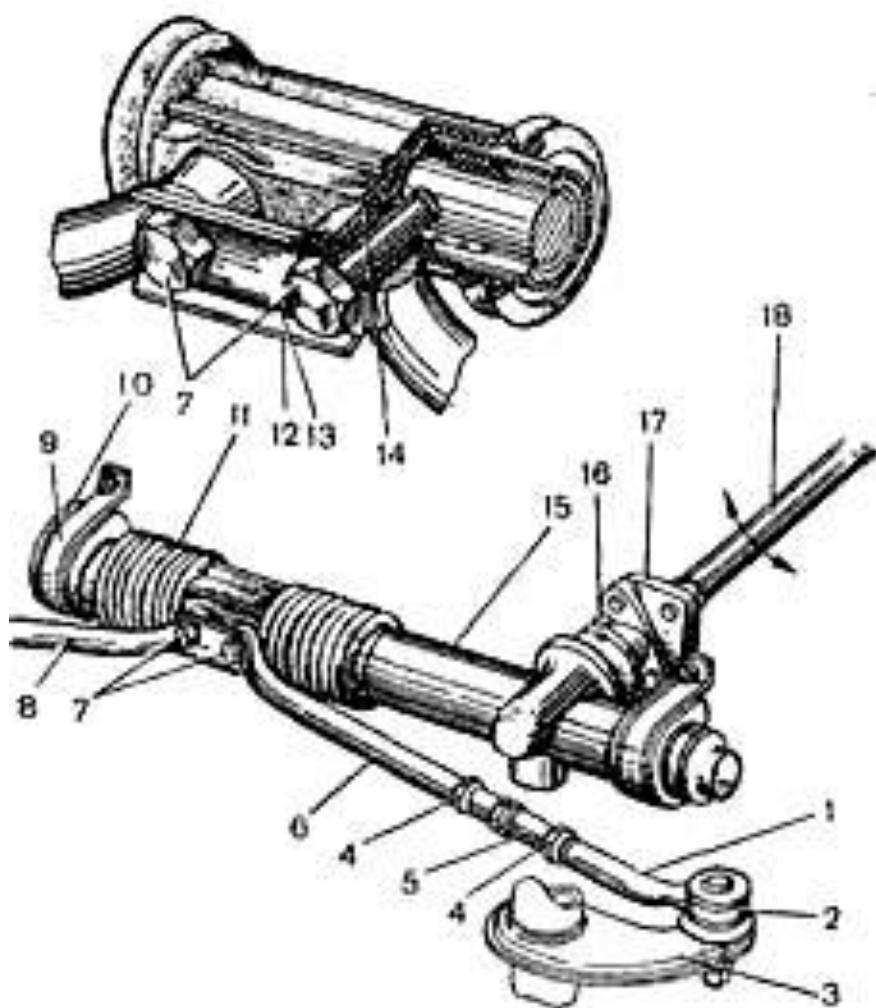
Рулевое управление автомобиля ВАЗ-2109: 1 — наконечник рулевой тяги; 2 — шаровой шарнир наконечника; 3 — поворотный рычаг; 4 — гайка; 5 — регулировочная тяга; 6 — рулевая тяга; 7 — болты крепления рулевых тяг; 8 — правая рулевая тяга; 9 — скоба крепления рулевого механизма; 10 — опора рулевого механизма; 11 — защитный чехол; 12 — соединительная пластина; 13 — стопорная
